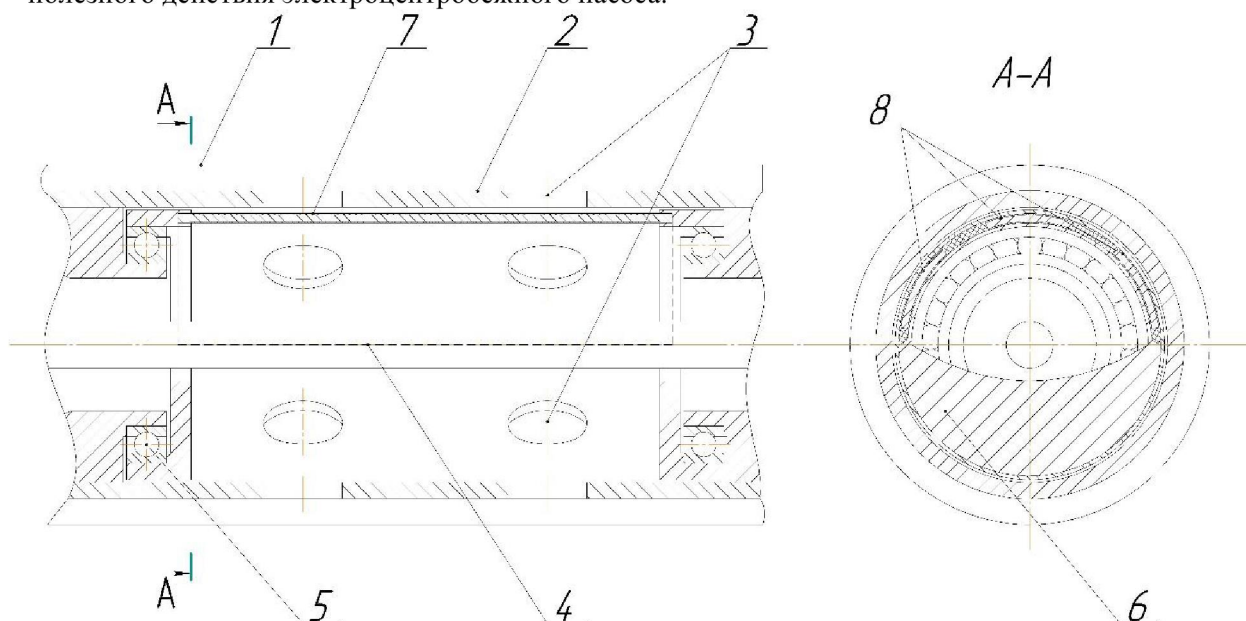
Схематическое изображение саморегулирующегося перекрывающего устройства: 1 – обсадная колонна, 2 – корпус, 3 – входные отверстия, 4 – вал, 5 – подшипники, 6 – балансирующий механизм, 7 – отсекающий элемент, 8 – металлический каркас
